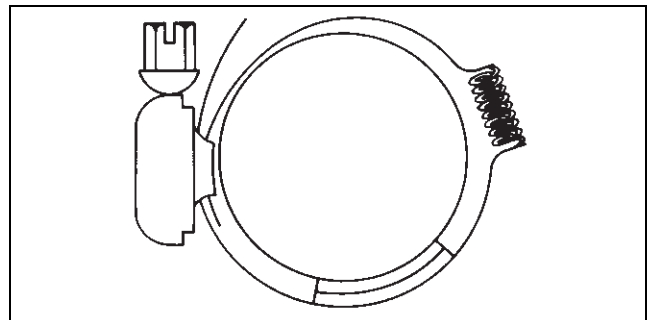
Schlauchklemme mit einer Feder in Serie, womit eine konstante und messbare Kraft erzeugt wird.
